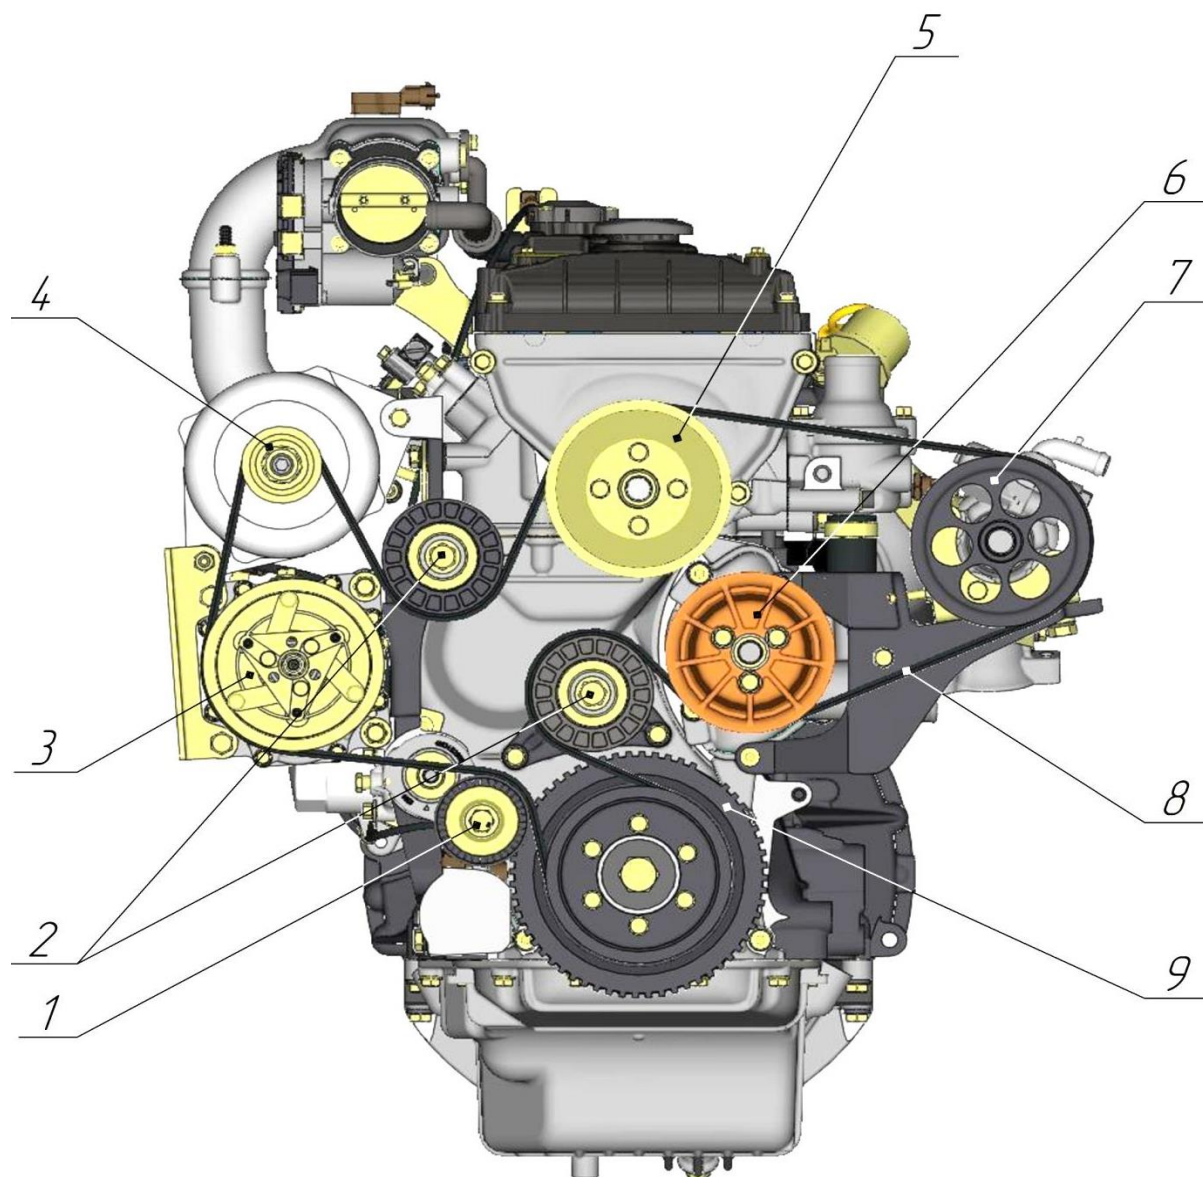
Вид спереди двигателя ЗМЗ-40905.10
